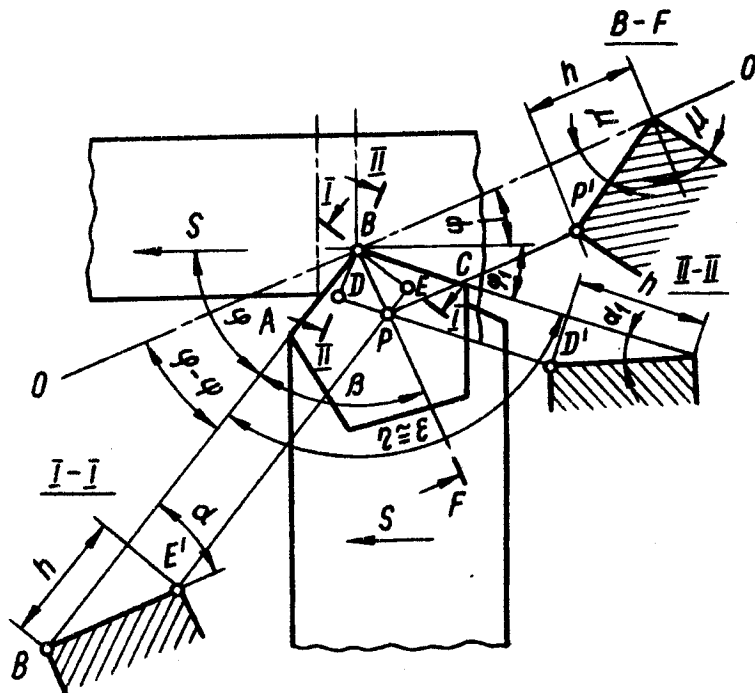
Схема установки багатогранної пластини на державці різця
